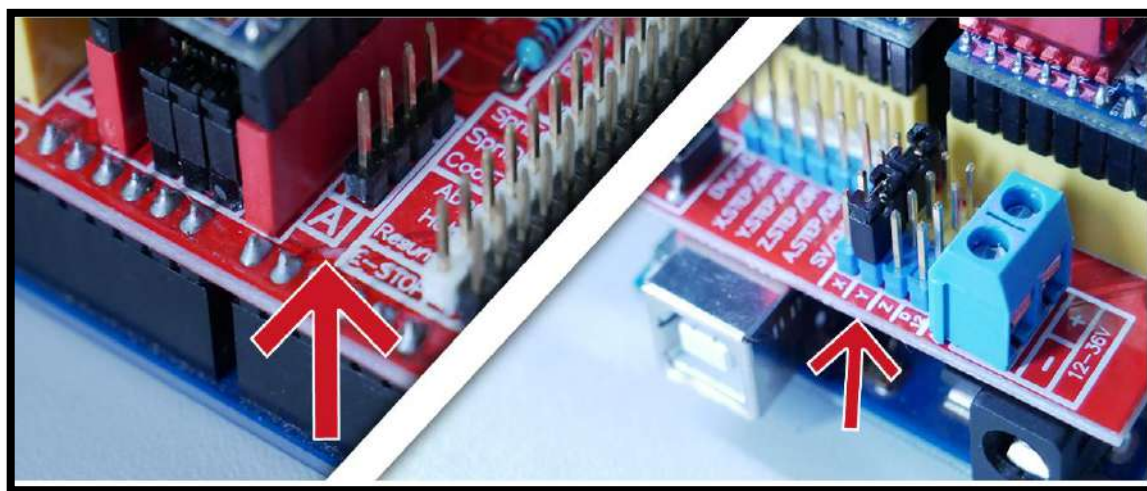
Endroit d'emplacement des jumpers sur la CNC Shield, pour répliquer un axe.
